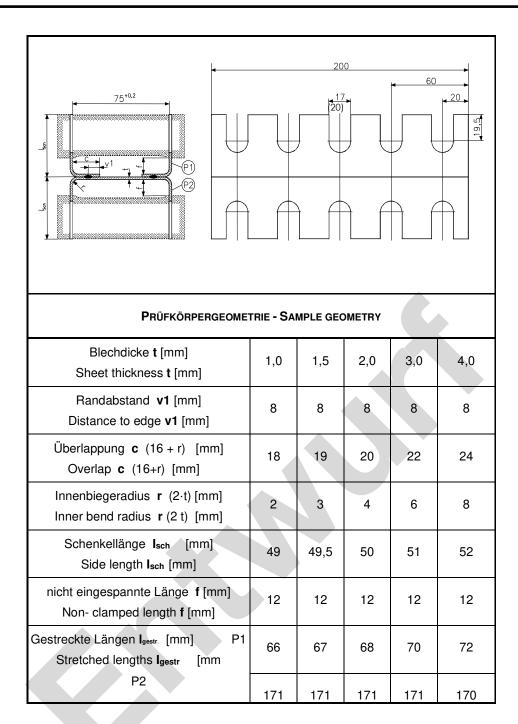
H-Schälzugprobe Widerstandspunktschweißen Figure 10: H-peel specimen resistance spot welding
